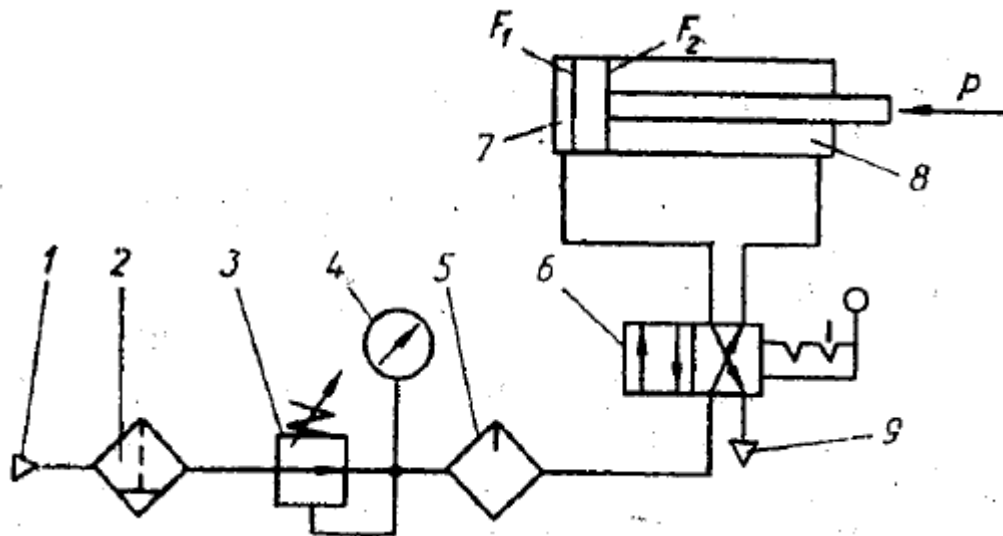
Схема пневматичного привода зворотно-поступальної дії
